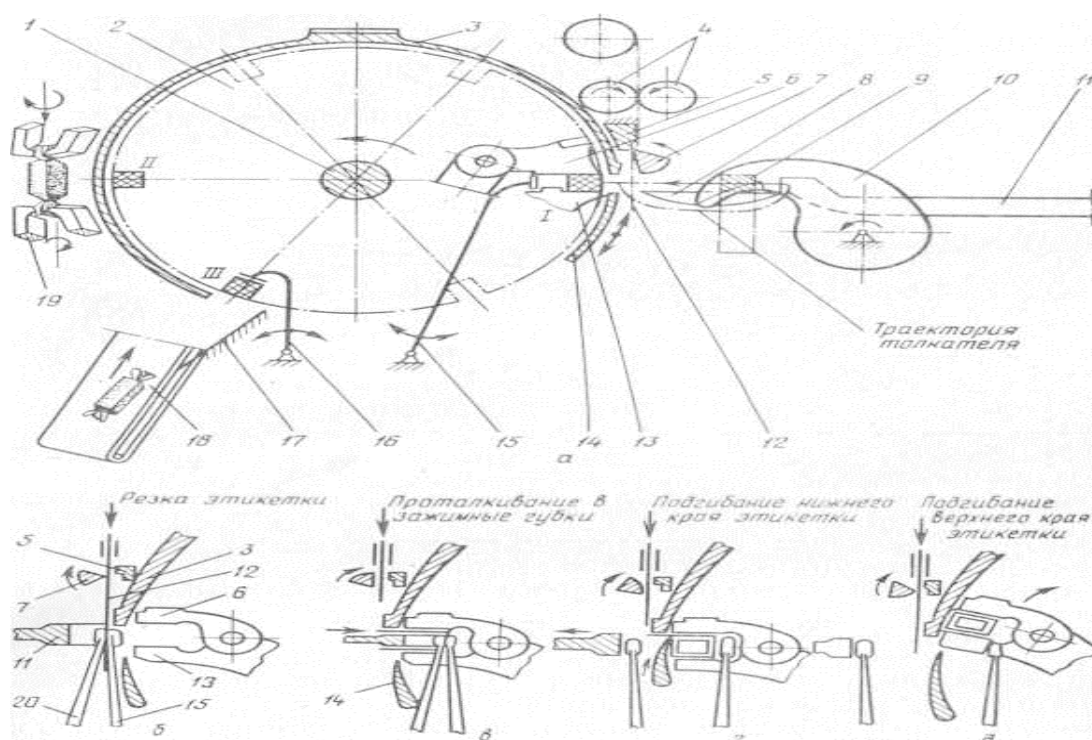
Механический формующий питатель автомата ИЗМ-1 для заправки карамели: а — рабочие позиции ротора; б, в, г, д — последовательность заправки в позиции I ротора
